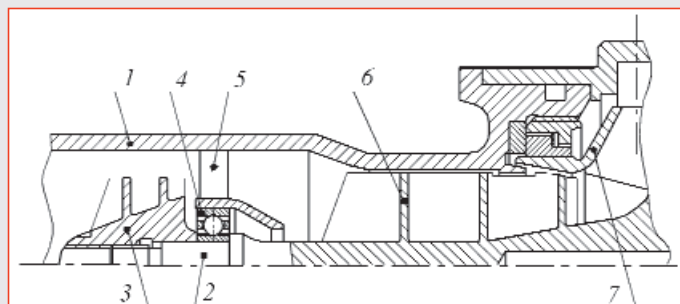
1 - корпус насоса, 2 - вал, 3 - бустерный шнек, 4 - подшипник, 5 - пилоны, 6 - предвключенный шнек, 7 - центробежное колесо
